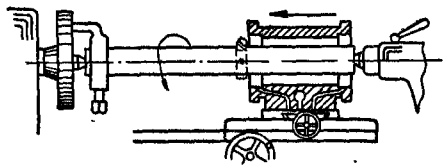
Схема растачивания отверстий в корпусе при помощи вращающейся скалки (оправки) с резцом.
